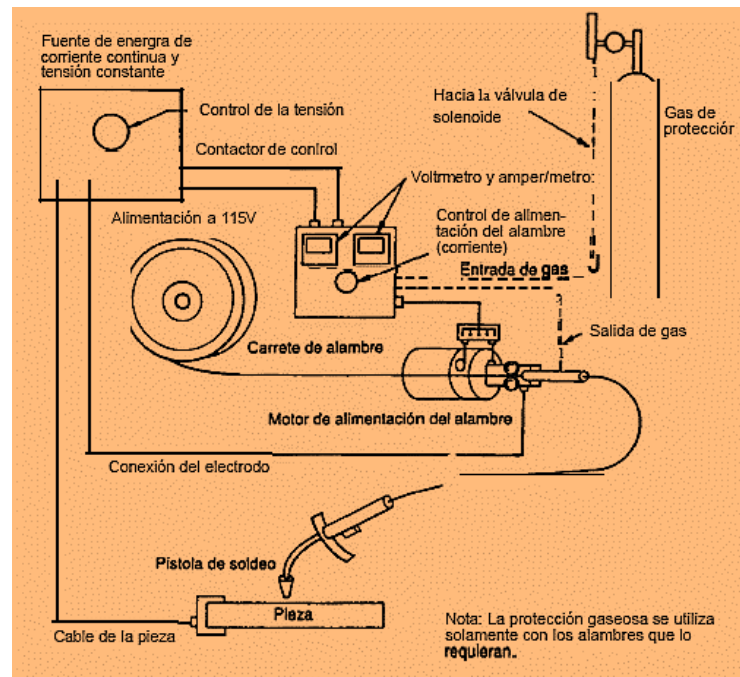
Equipo para soldadura por arco con alambre tubular.
